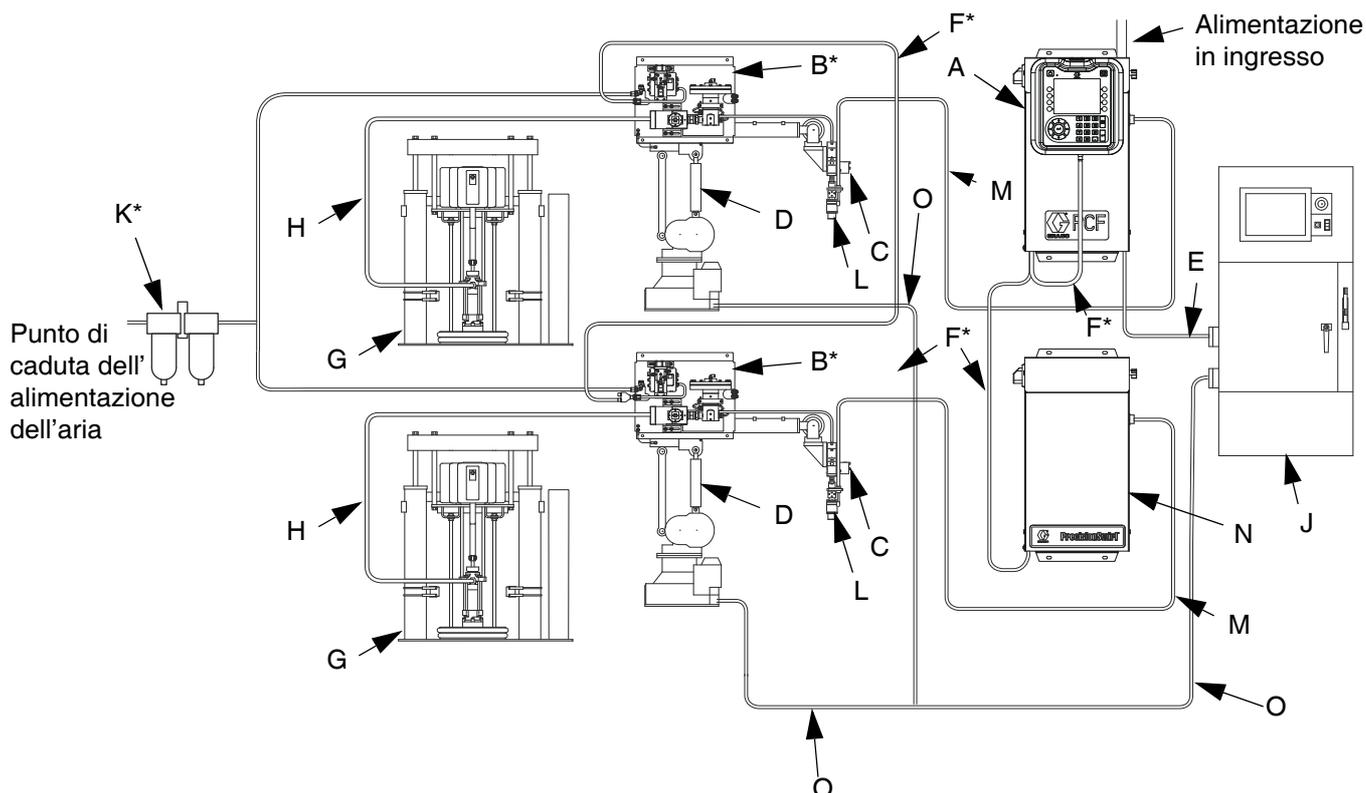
Installazione tipica del sistema con più piastre del fluido
